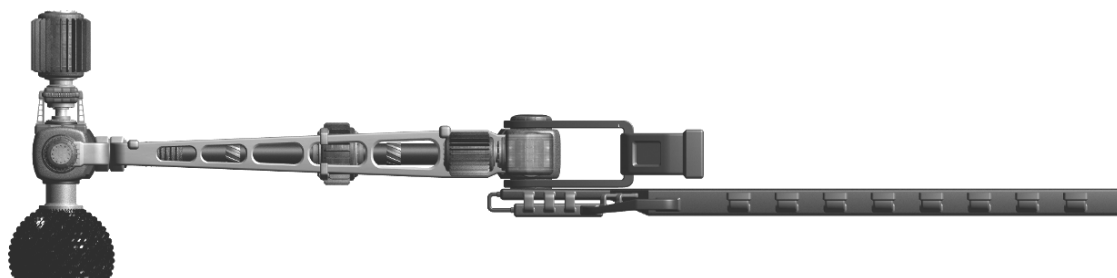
Многоосная подвижная консоль с фрезой (слева). Крепления к корпусу лунохода, и устройство подачи реголита (справа)
